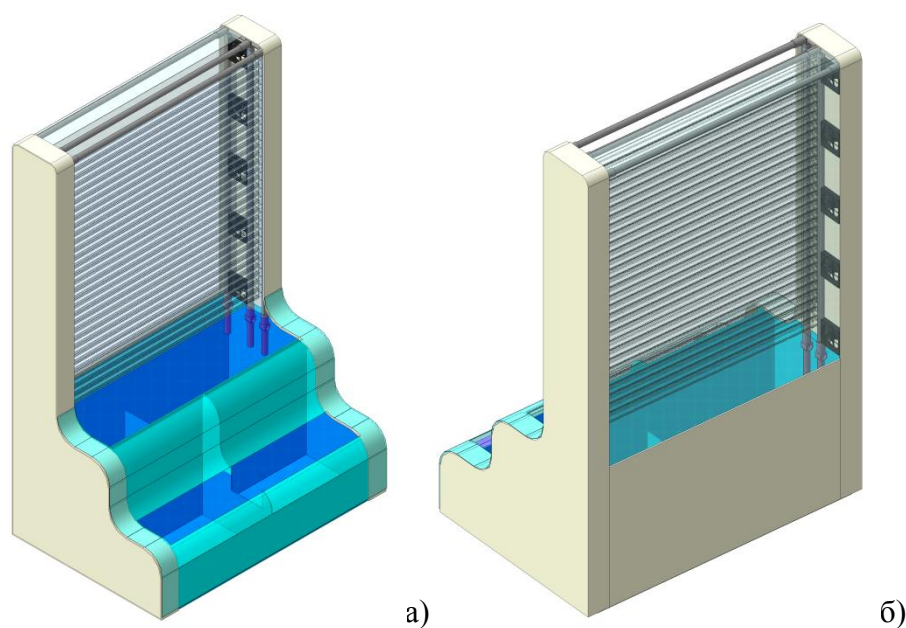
Чертеж защитной дезинфицирующей ширмы двойного назначения в сборке, вид спереди (а) и сзади (б)
